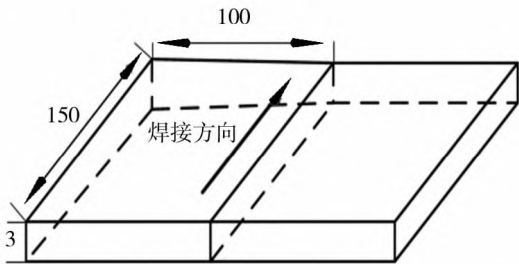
试验基体与焊接方向示意图(单位:mm)
